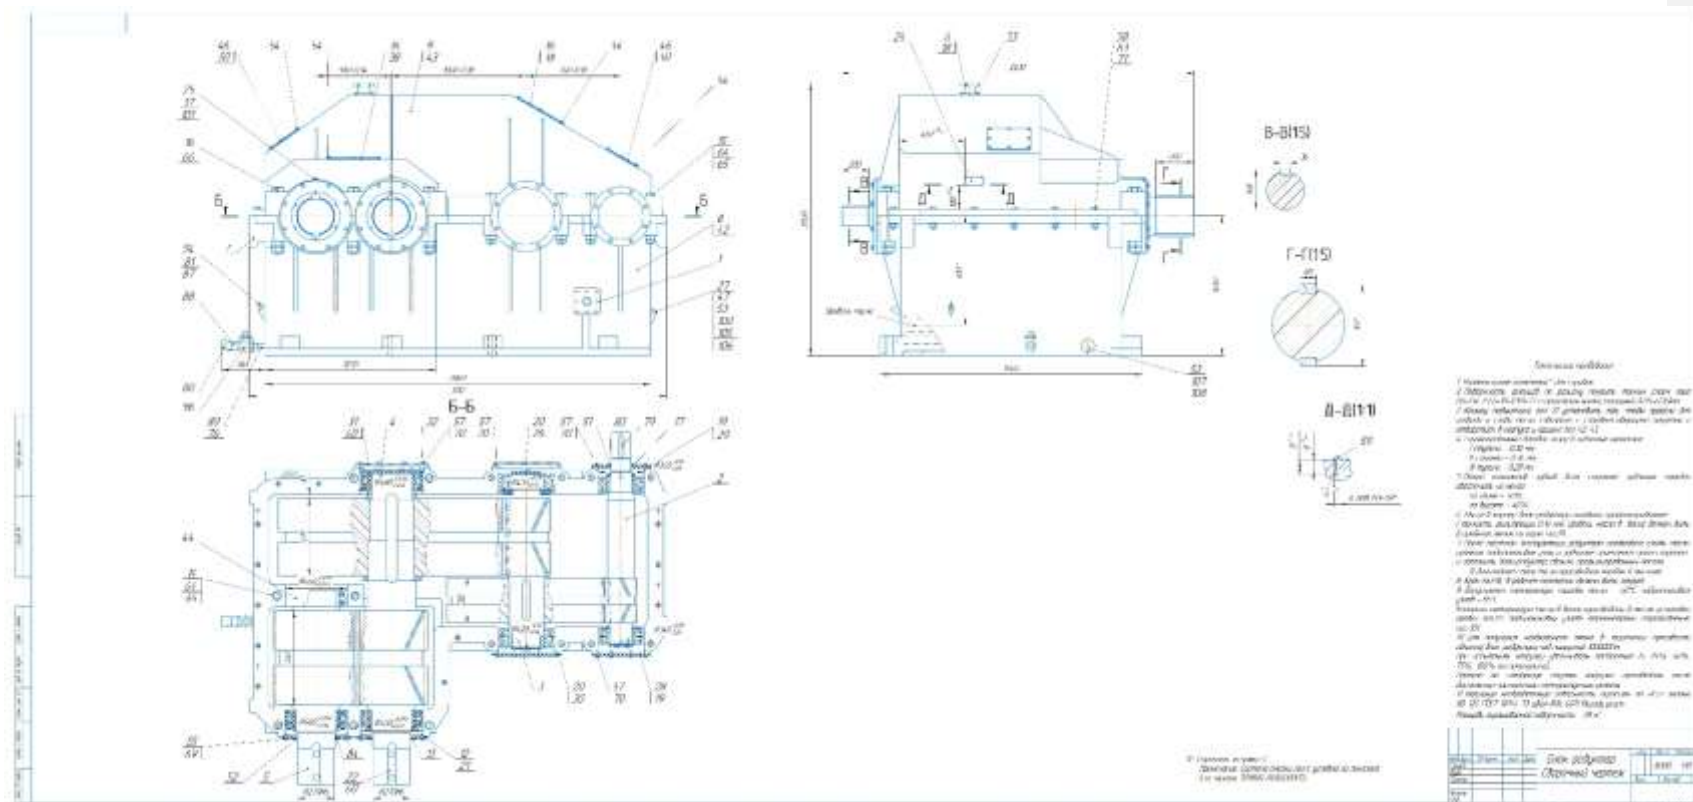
Складальне креслення циліндричного редуктор.
